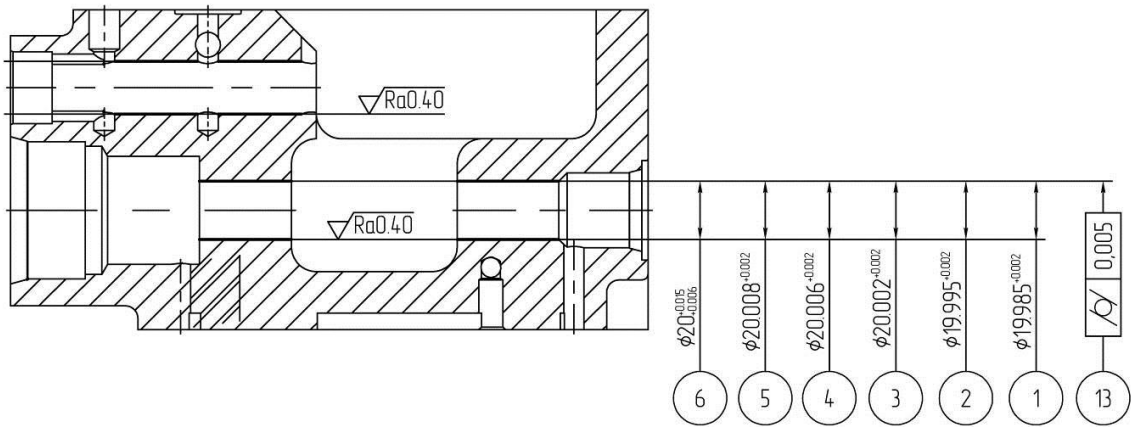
Розміри оброблюваного отвору корпусу гідророзподільника
